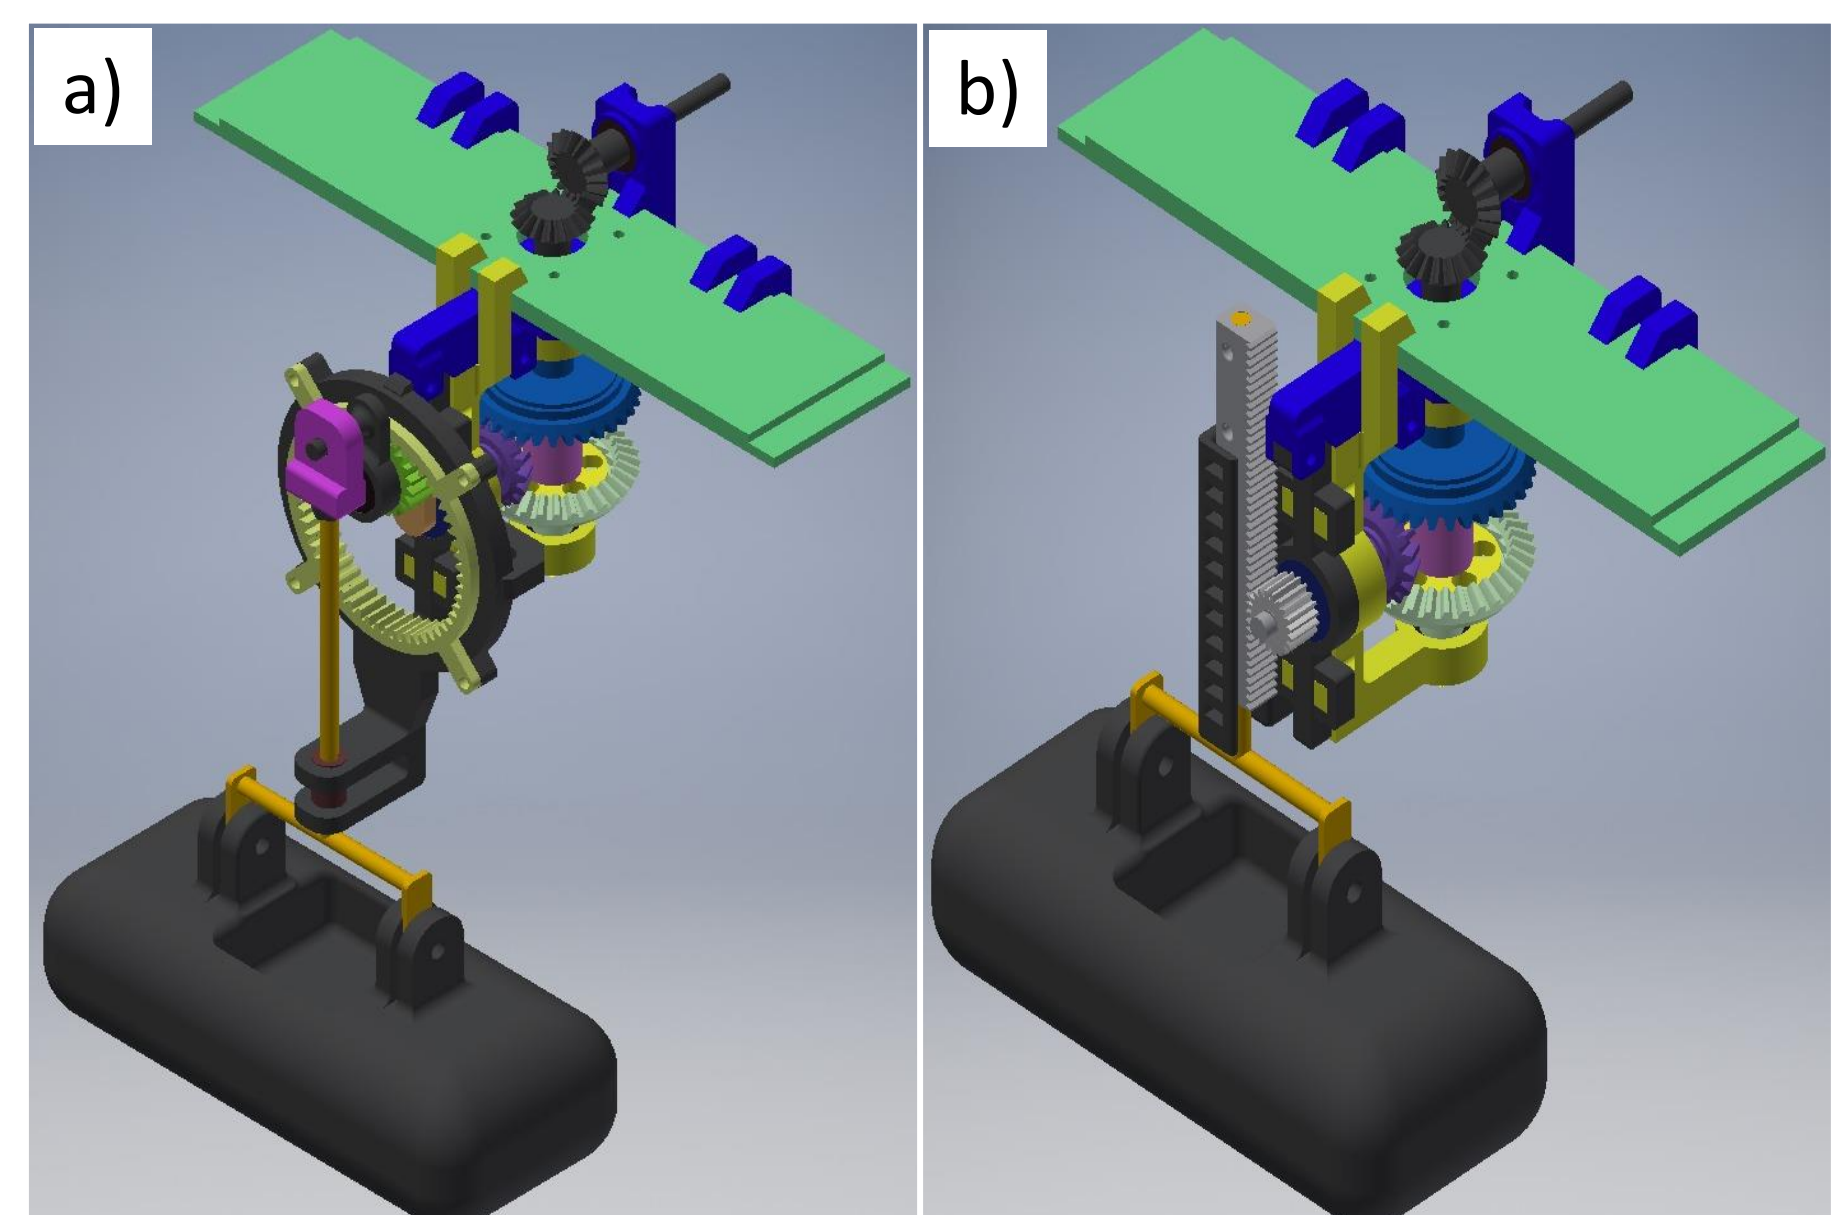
Diseño CAD del prototipo. a) Diseño inicial. b) Rediseño
